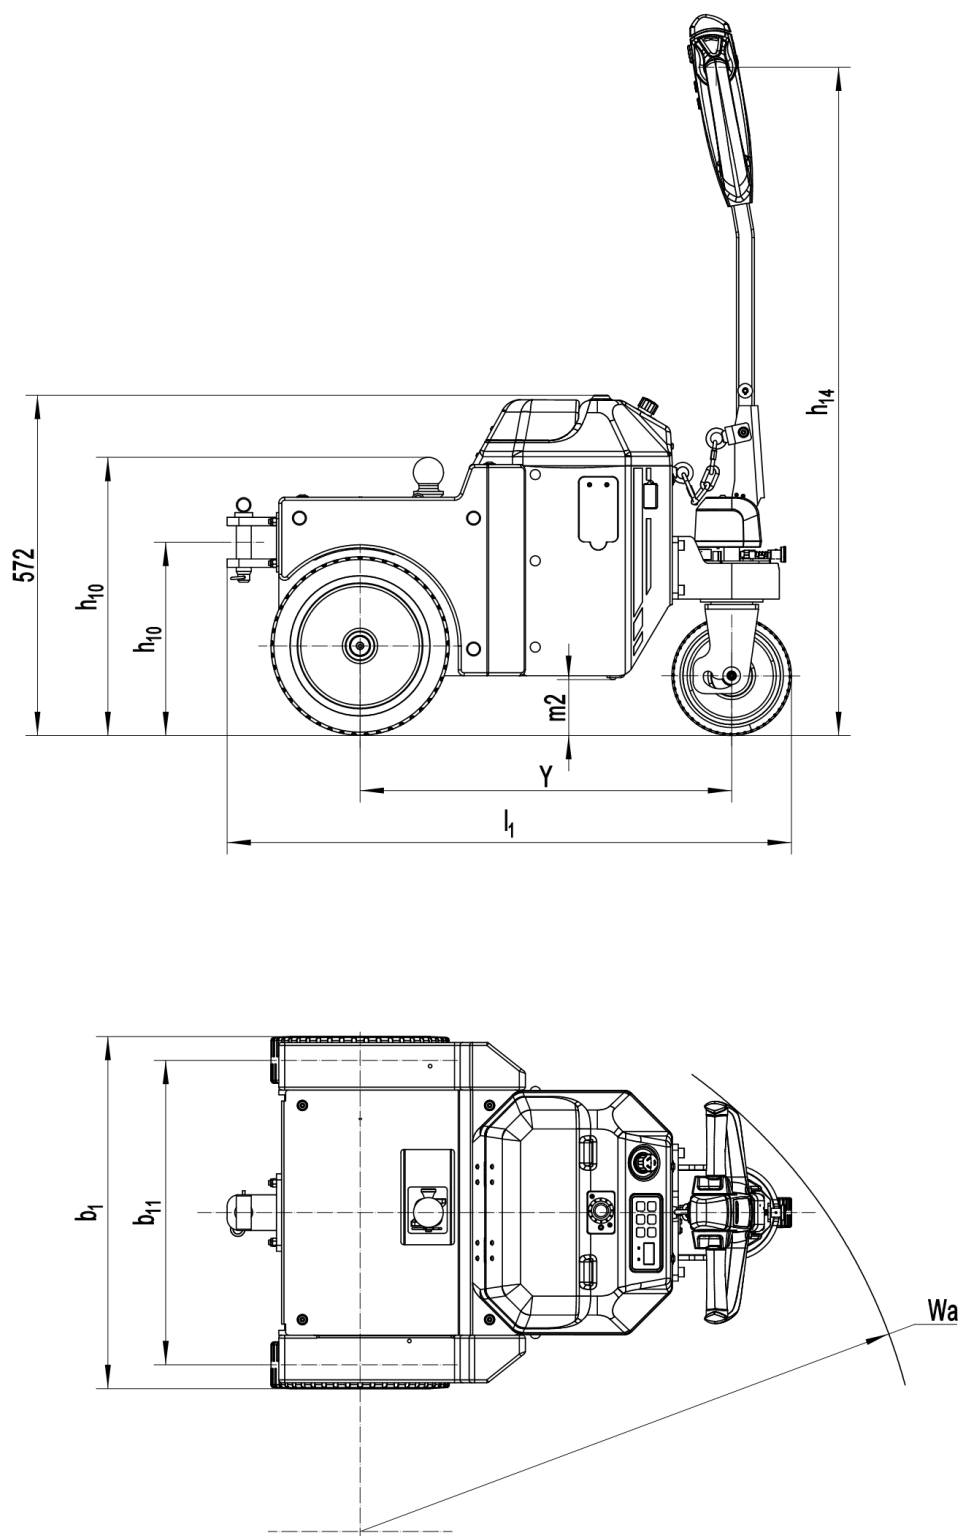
Схематический чертеж конструкции (TWS-300i)
